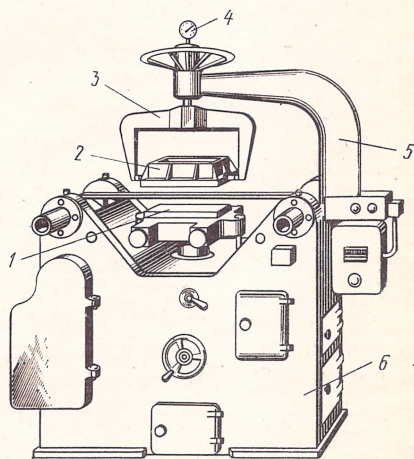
Плоскопритирочный двухплитный станок конструкции Д. С. Семенова
